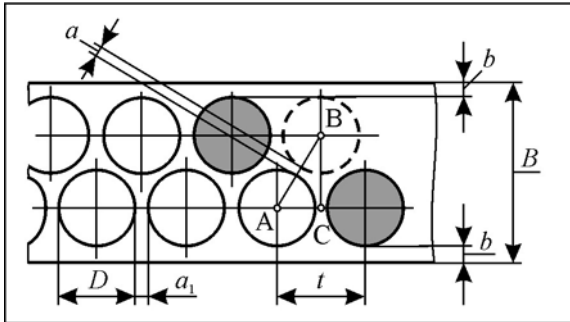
Схема дворядного шахового розкрою стрічки
